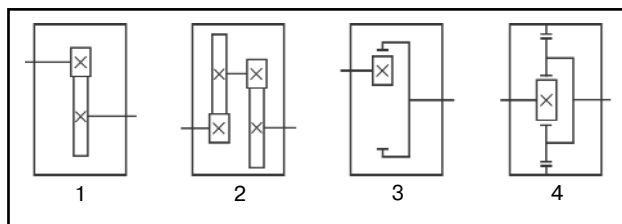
Варианты конструктивных исполнений цилиндрической ступени
